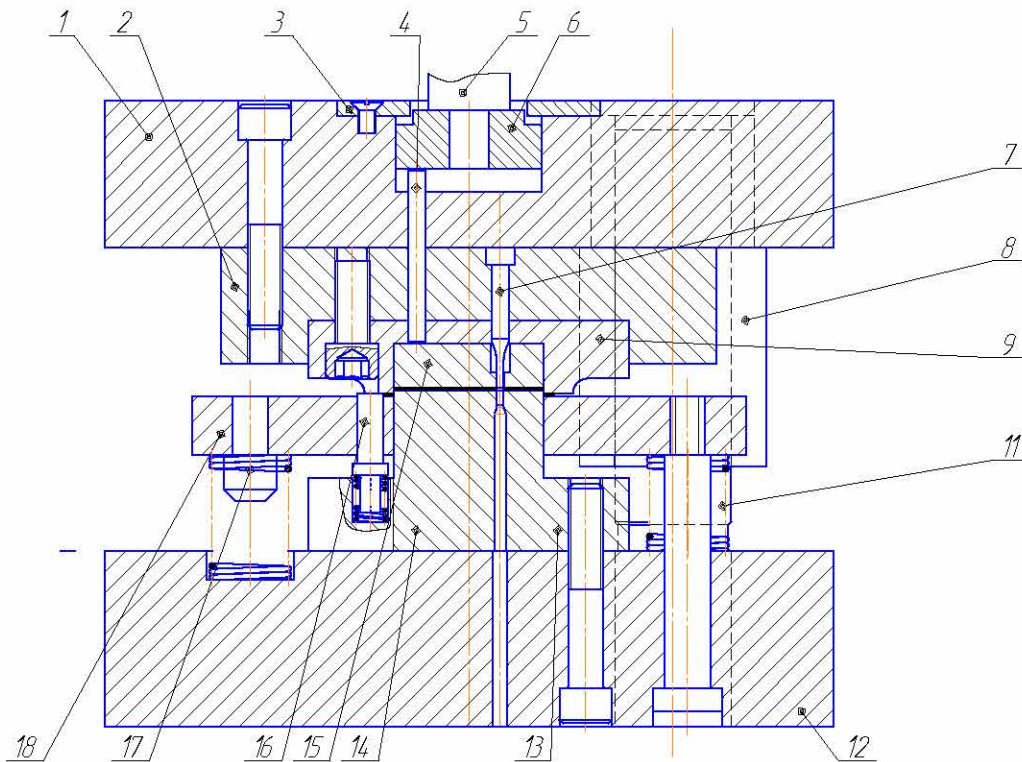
Схема штампа для вирубаня-пробивання деталі „Скоба”
